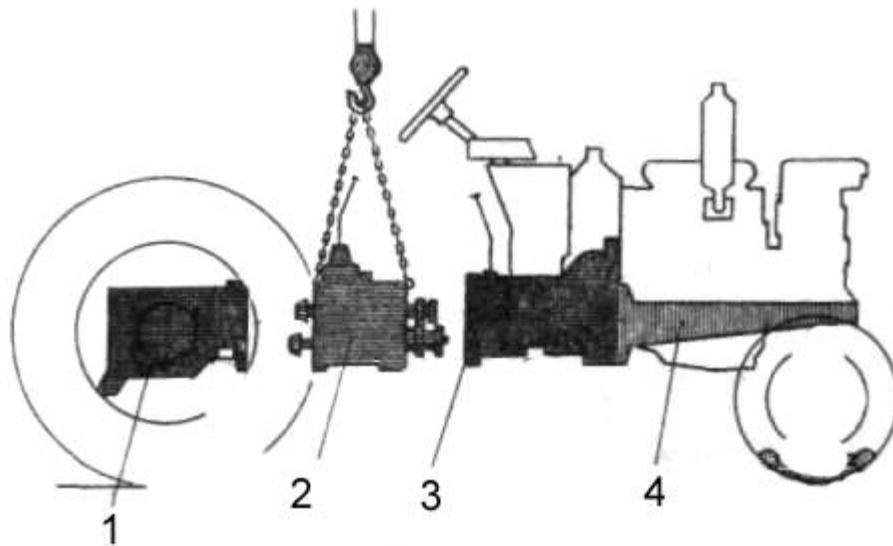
Схема від’єднання та знімання коробки передач:
